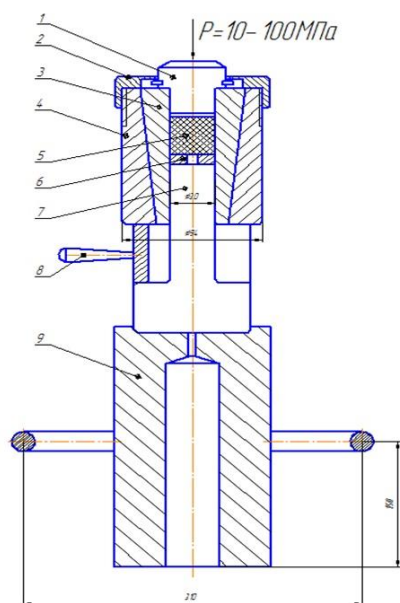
Схема сбора пресс-формы для СВС-экструзии
